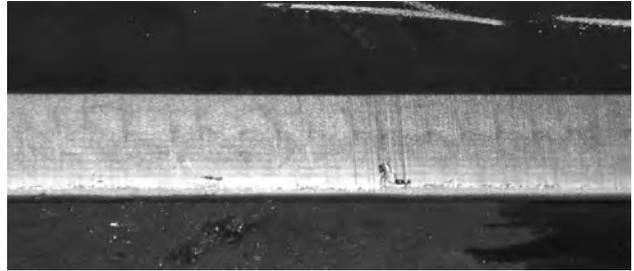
Стенд для снятия фасок под сварку. Резка производится снизу - вверх под углом 60° к горизонтали. Поверхность реза
